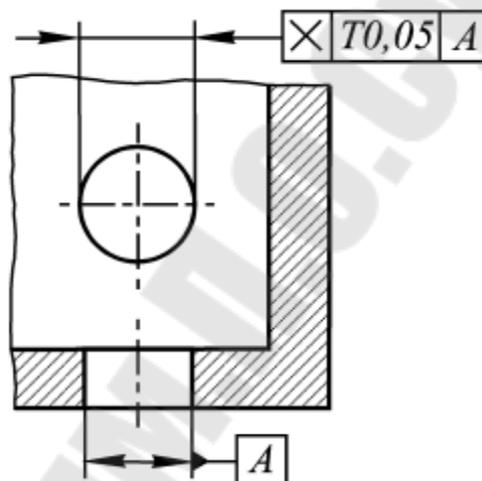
Допуск на отклонение от пересечения осей
